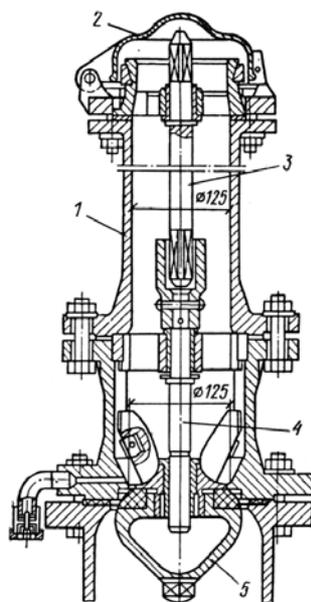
Гидрант пожарный подземный: 1 – чугунный корпус; 2 – крышка; 3 – штанга; 4 – шпindelь; 5 – затвор с клапаном обтекаемой формы
